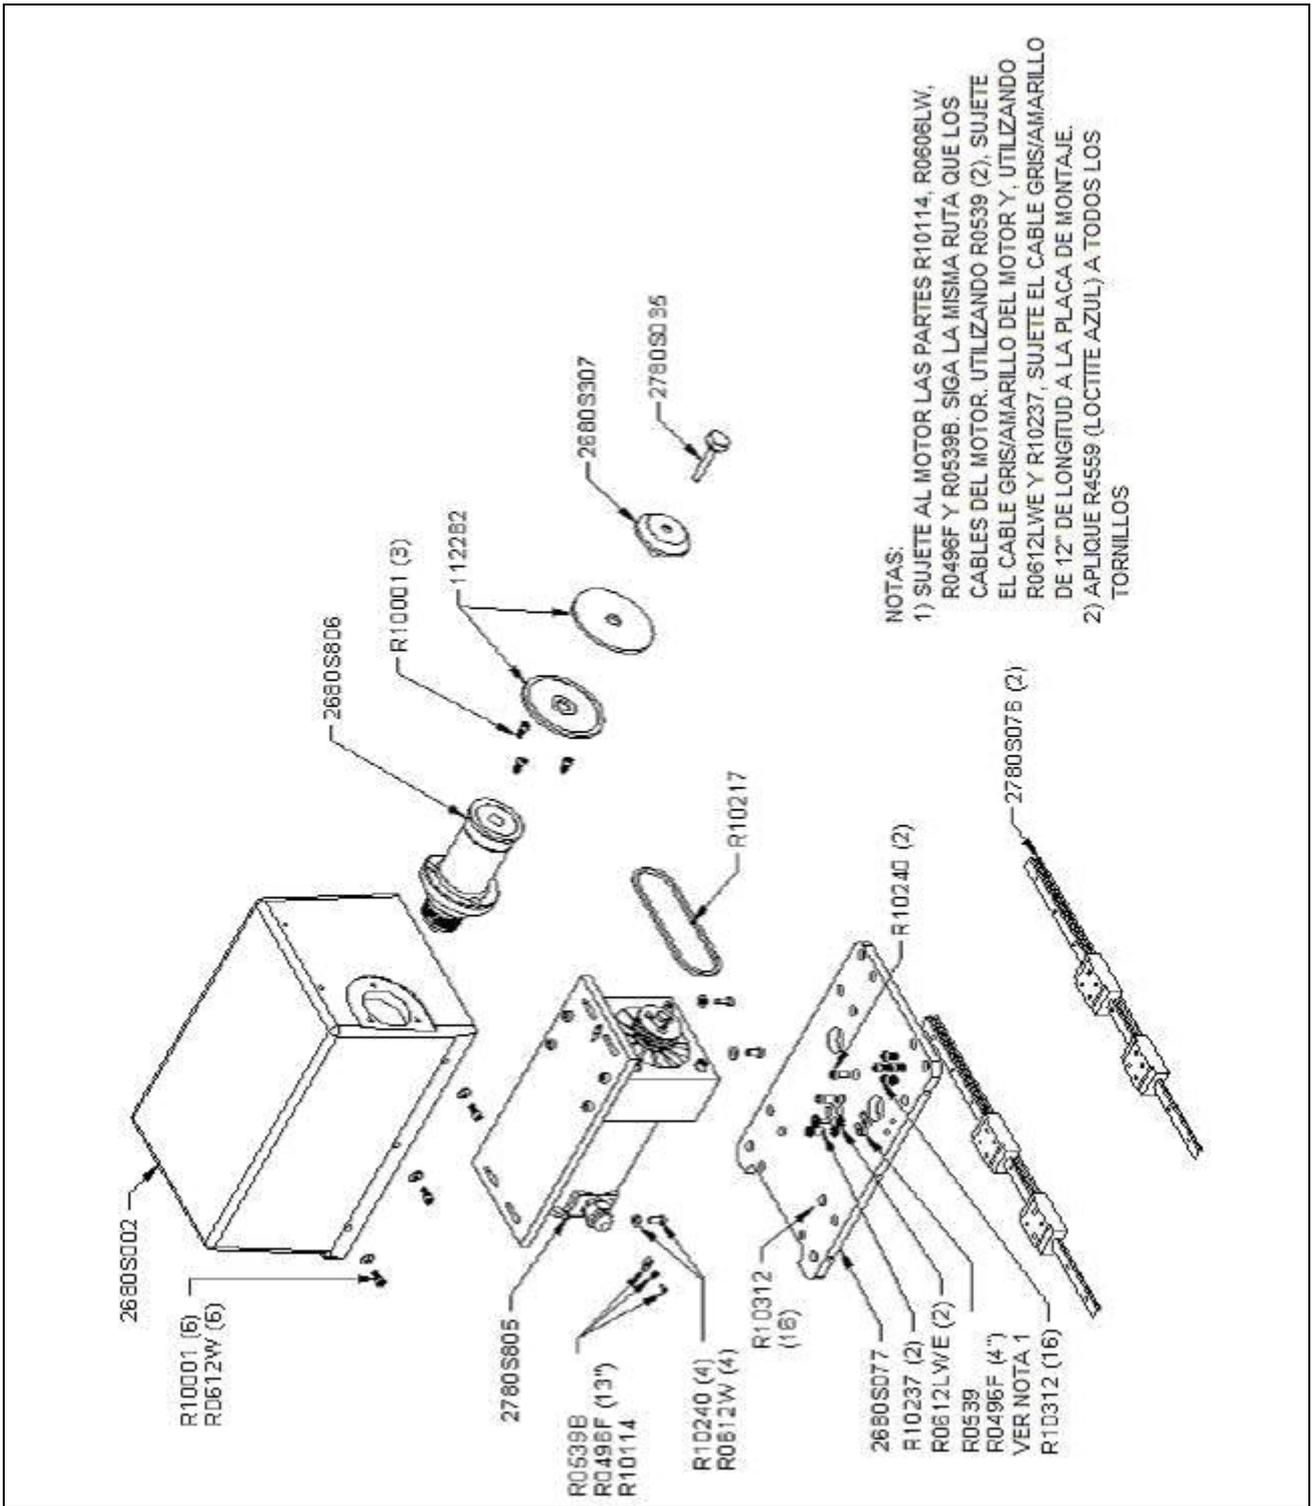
Dibujo de despiece de la torreta del disco de corte (2780S800).
